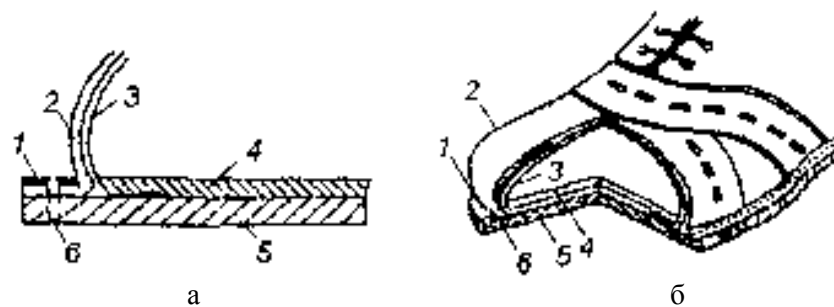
Допдельный метод крепления: а – схема крепления; б – разрез обуви: 1 – рант, 2 – наружные детали верха, 3 – подкладка, 4 – основная стелька, 5 – подошва, 6 – ниточный шов
